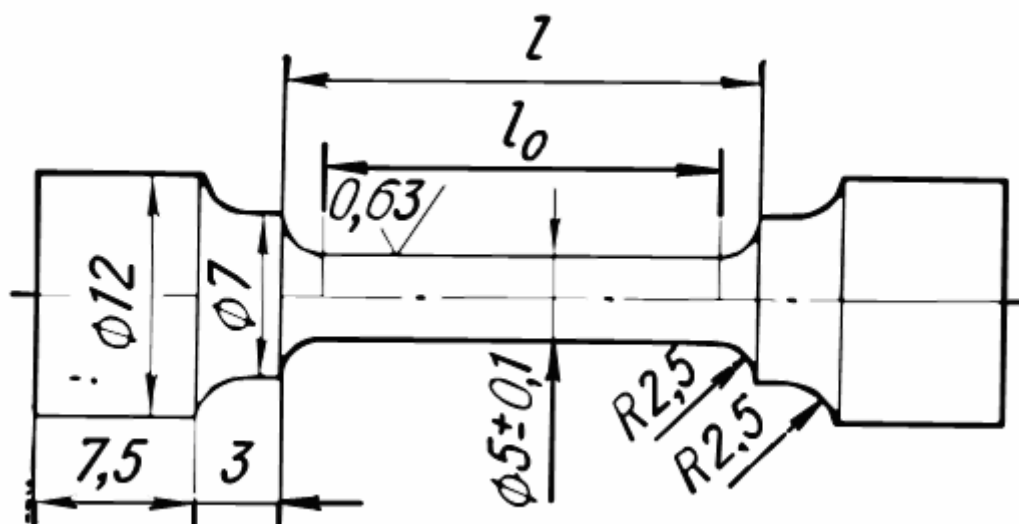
Стандартный цилиндрический образец для испытаний на растяжение
